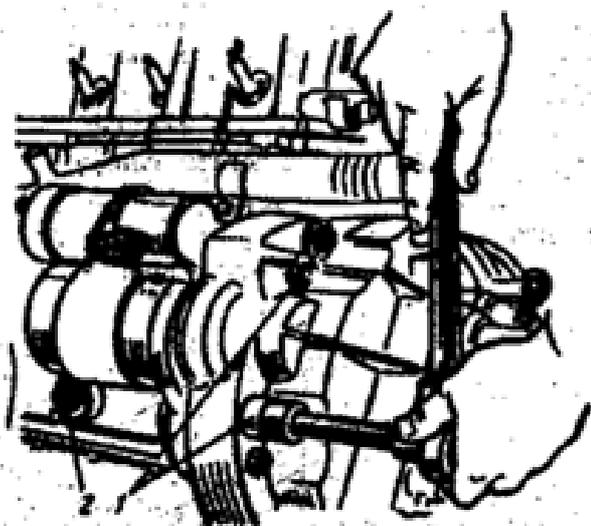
Отворачивание гаек крепления стартера и его снятие: 1-гайки крепления стартера; 2-датчик верхней мертвой точки
